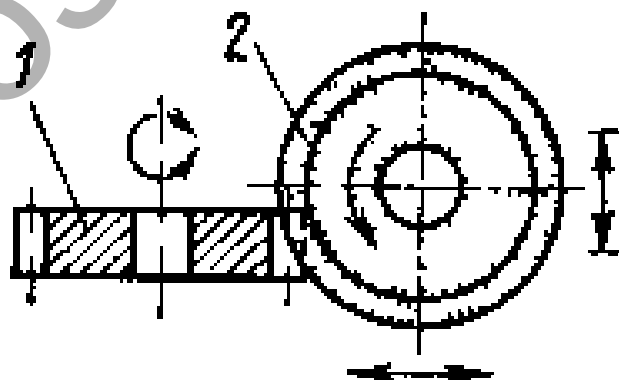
Схемы шлифования зубчатых колес плоским кругом, которому придана форма зуба рейки
